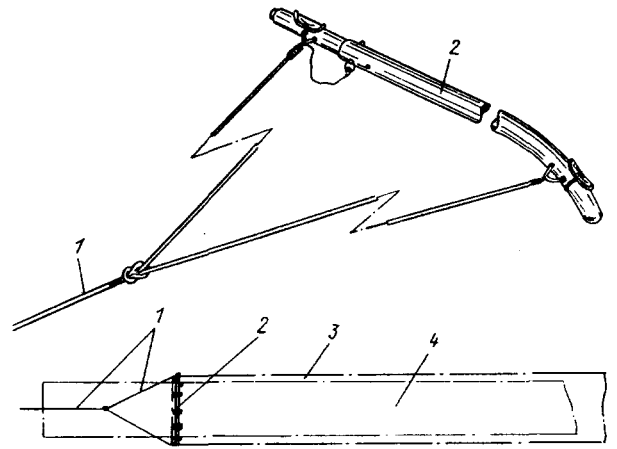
Приспособление для надевания чехлов на лопасти несущего винта:
